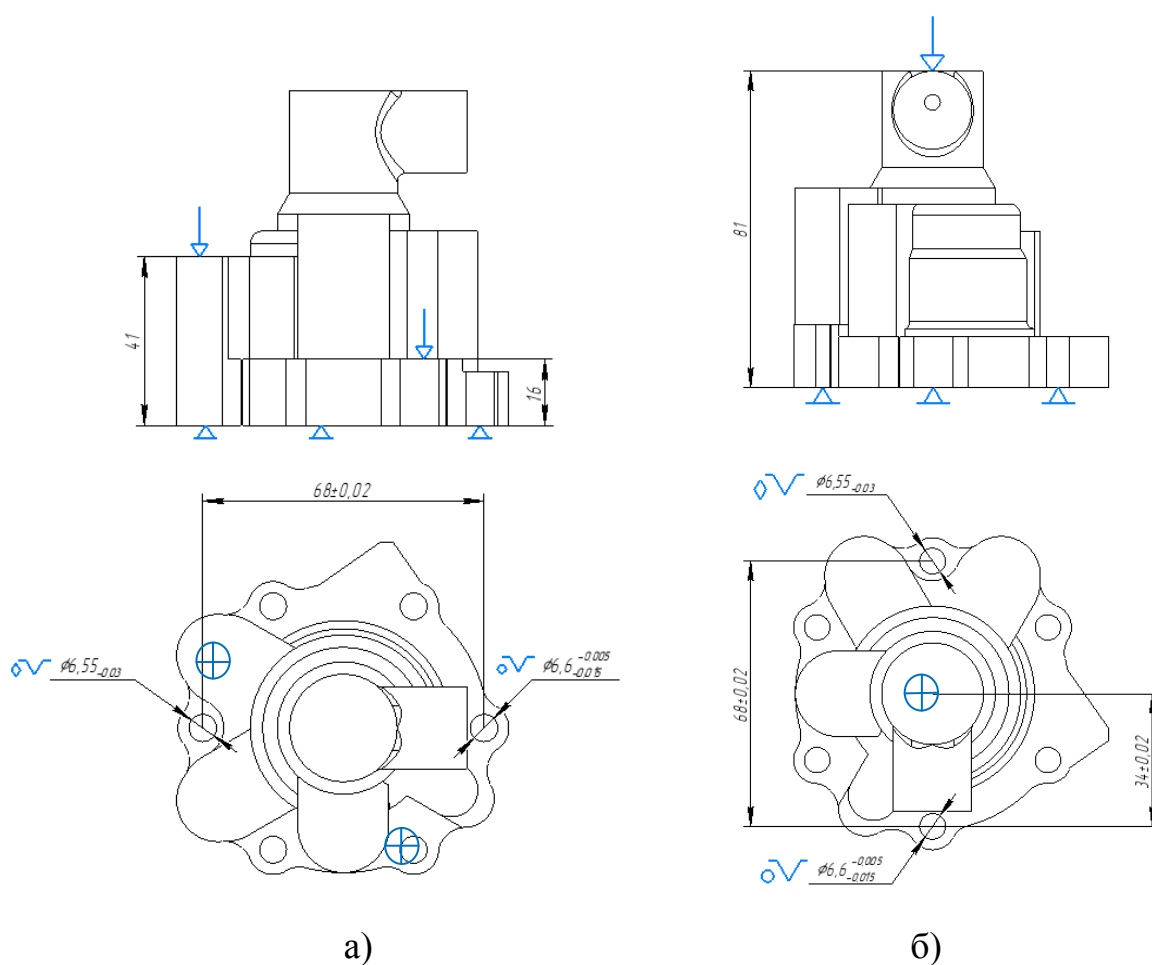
Схема закрепления заготовки на установке 1 (а) и установке 2 (б)
